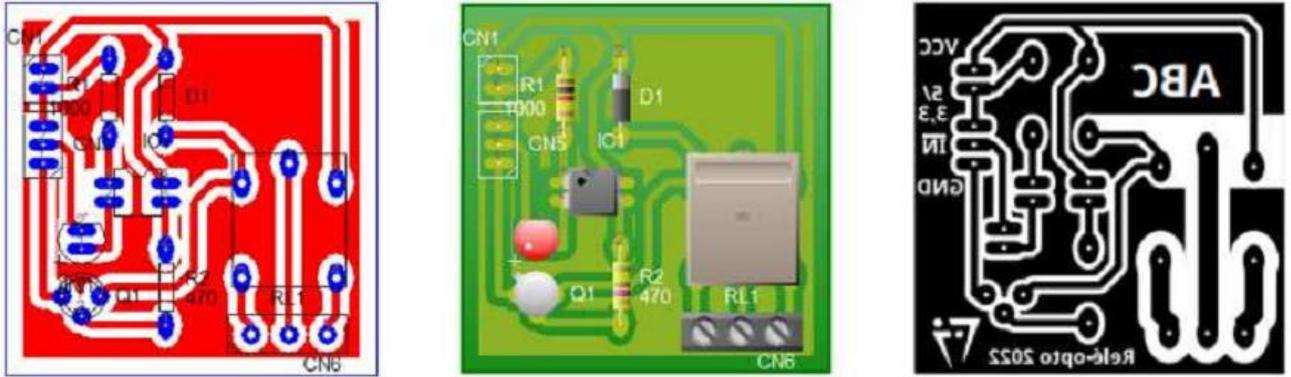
Diseño asistido por computadora PCB Wizard – Relé GAX1
